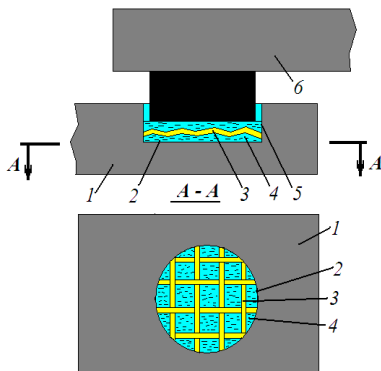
Композиционный жидкометаллический контакт с сетчатой основой: 1 – неподвижный контактодержатель; 2 – углубление; 3 – сетчатая основа; 4 – жидкий металл; 5 – выступ; 6 – подвижный контактодержатель (мостик)
